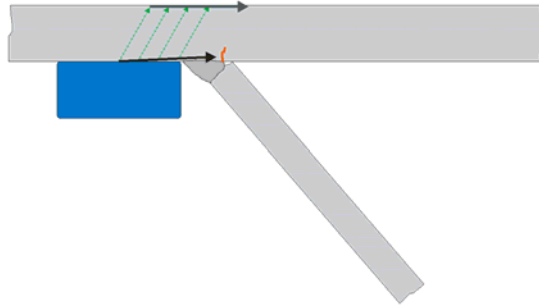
Detektion einer Rissbildung mittels Kriechwellen.
